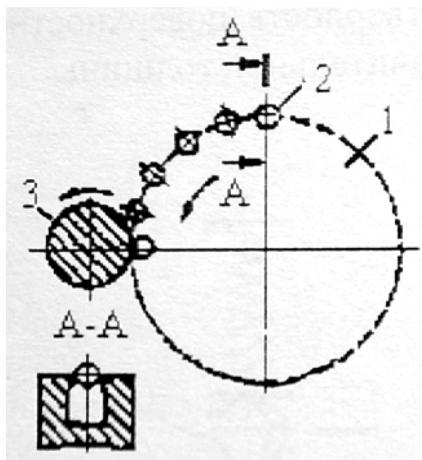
Схема центробежно-шариковой упрочняюще-чистовой обработки: 1 – диск; 2 – шарики; 3 – обрабатываемая деталь
